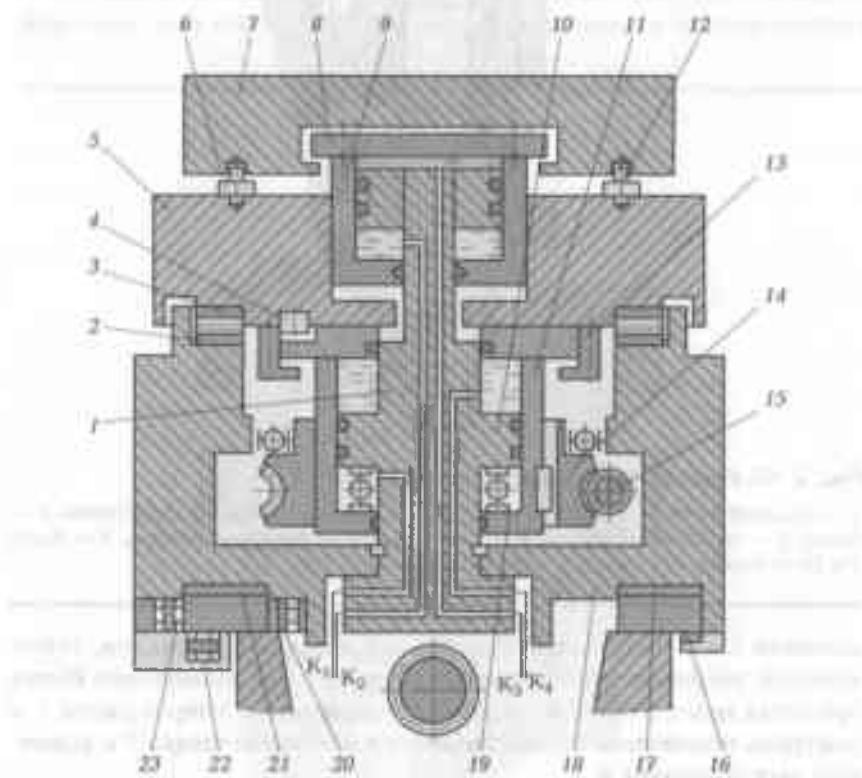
Привод поворотного стола многоцелевого станка:
